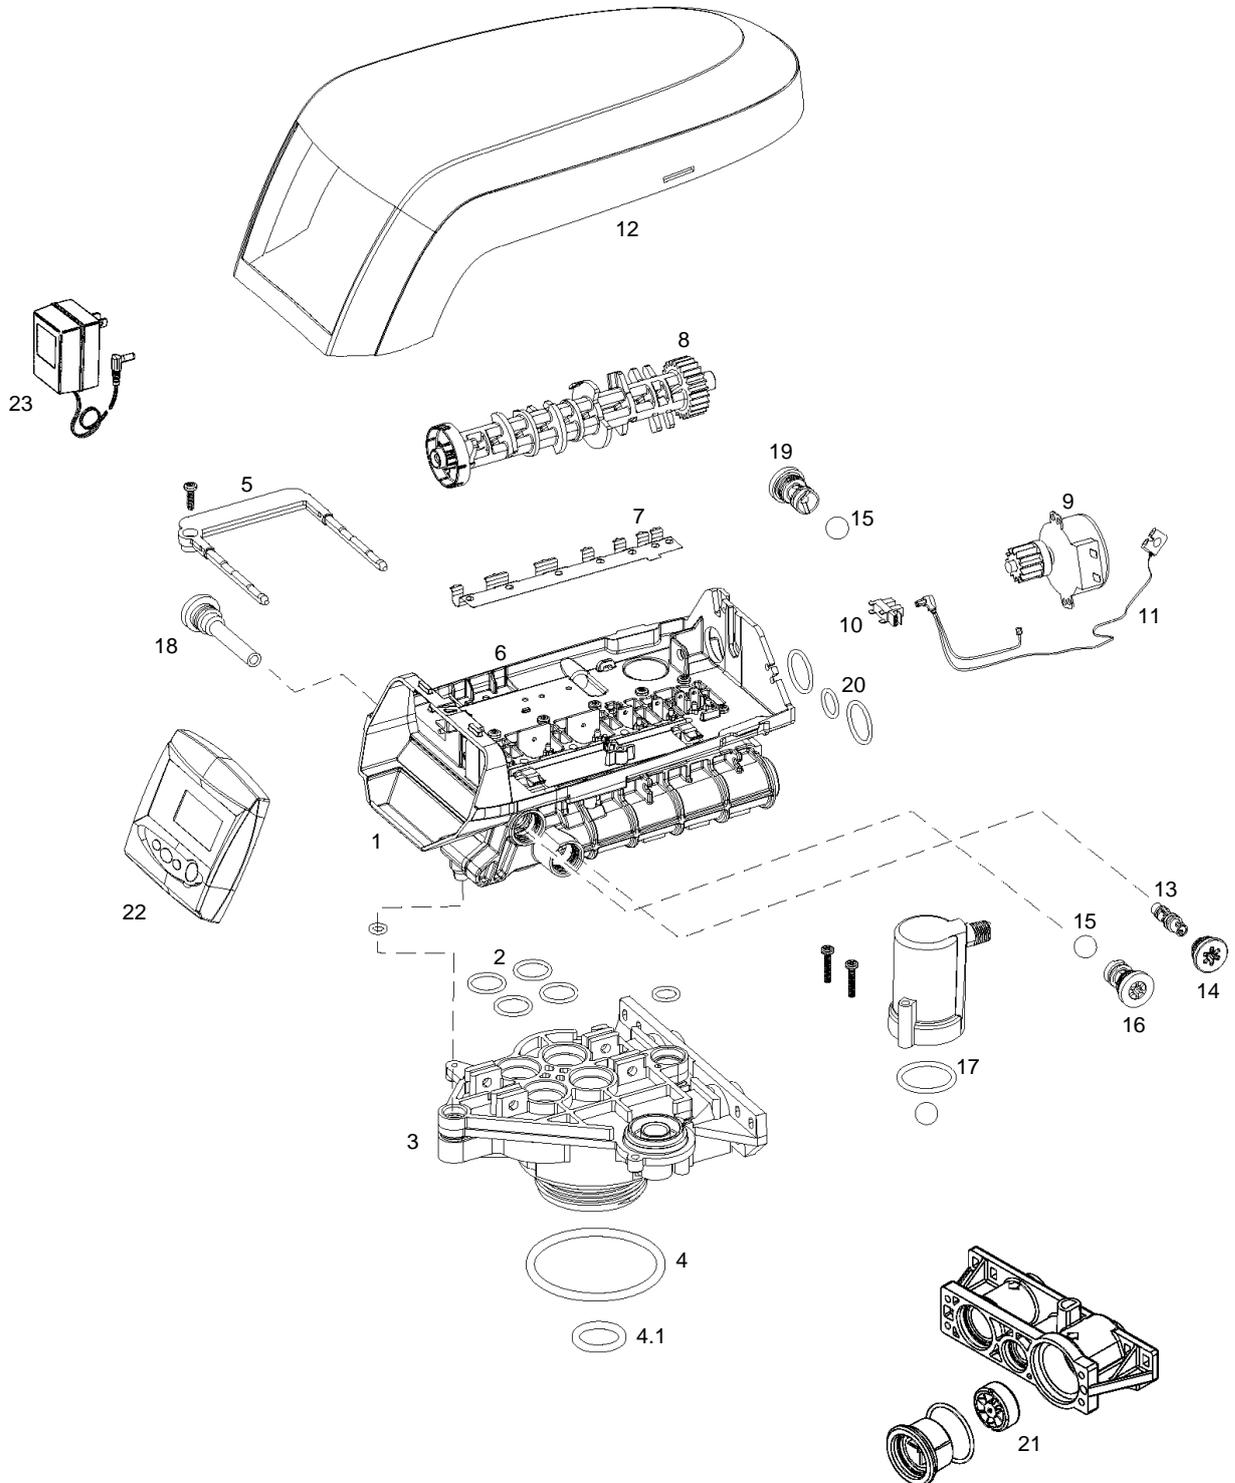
Explosionszeichnung Zentralsteuerventil JDN 1-3 WZ-E
